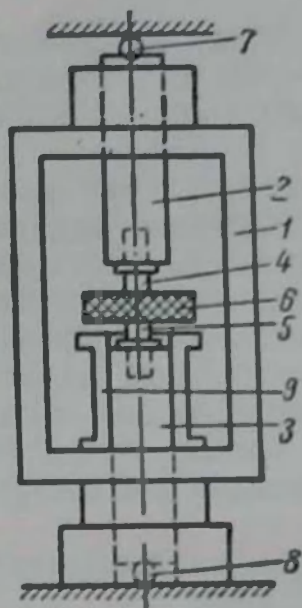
Конструкция приспособления для точного соосного расположения пуансонов:
